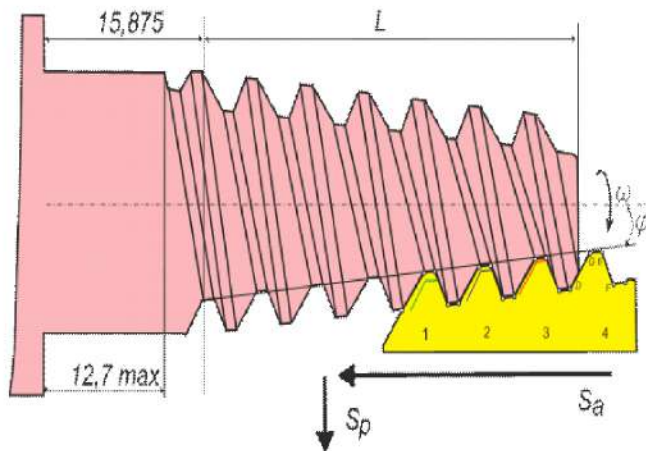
Схема початку фінішного проходу 4-ниткової гребінки під час виконання замкової нарізи. Sa - повздовжня подача гребінки, Sp - поперечна подача гребінки, ω - рух обертання заготовки навколо осі.
